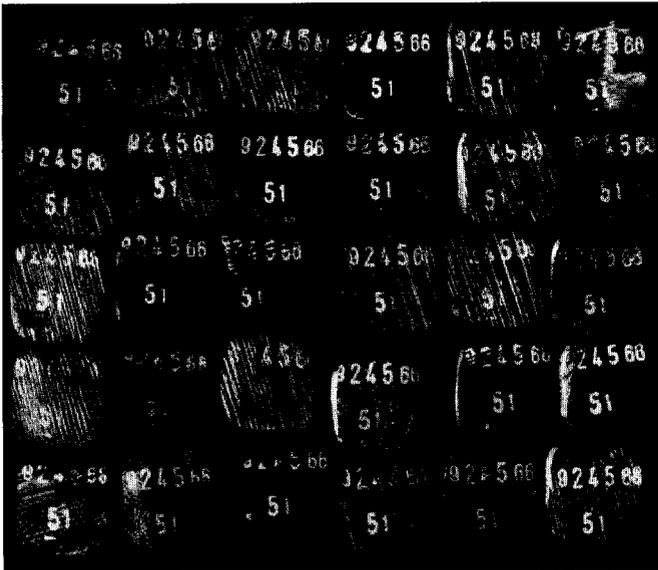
Kennzeichnung von Schmiedematerial im Halbzeuglager
